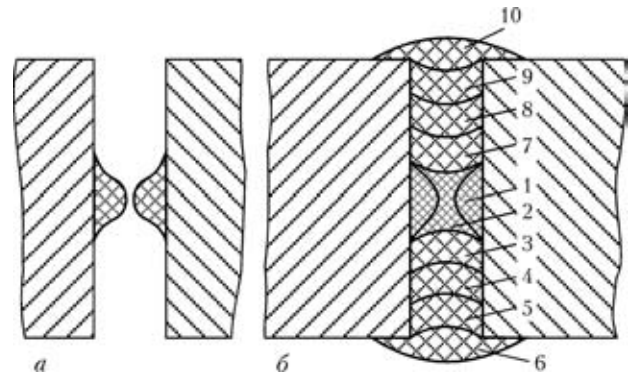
Схема последовательности выполнения сварки по щелевому зазору: а — соединение с наплавками, собранное под сварку; б — порядок выполнения проходов (обозначен цифрами)
